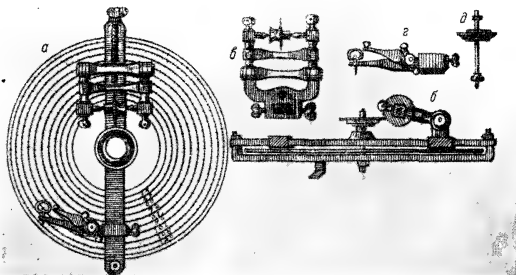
Устройство для фрезерования часовых зубчатых колес. Нач. XVIII в. По Н. Биону.
